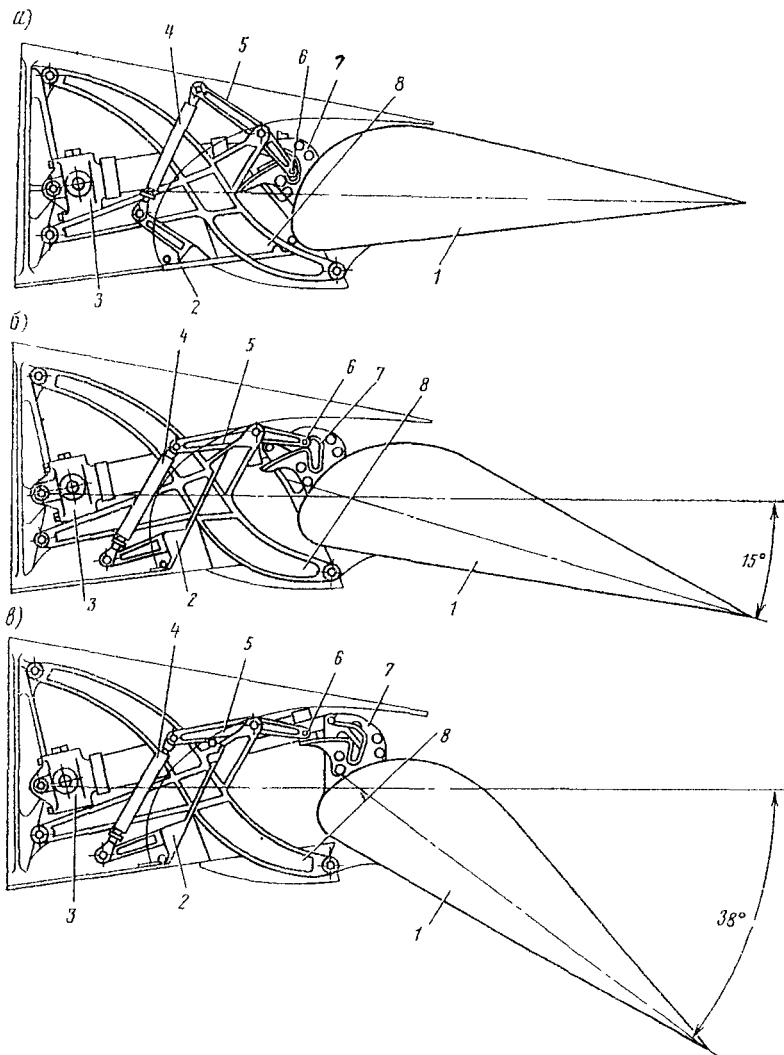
Схема уборки и выпуска закрылка в центральной части крыла:
